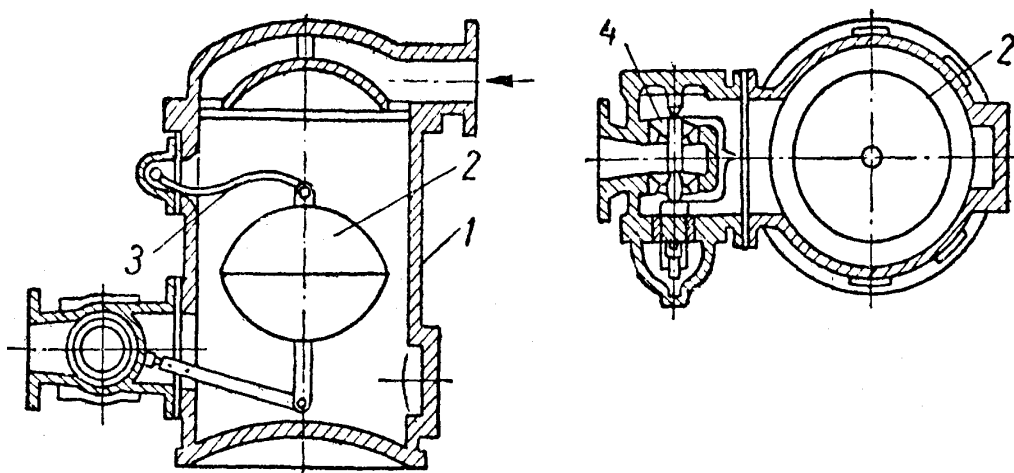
Конденсатоотводчик с рычажной передачей и двухседельным клапаном: 1 – корпус; 2 – поплавок; 3 – рычаг; 4 – двухседельный клапан
